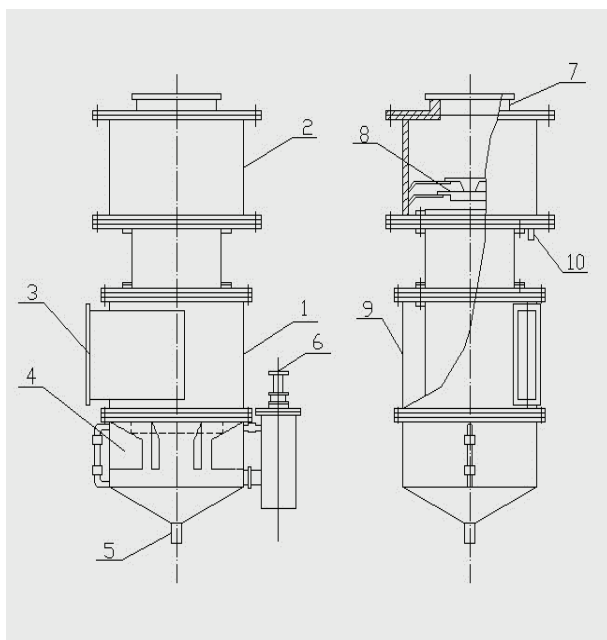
Схема инжекционно - пенного аппарата II - ой ступени очистки: 1 - корпус аппарата, 2 - корпус влагоотделителя, 3 - тангенциальный патрубок, 4 - лопаточный закручиватель, 5 - штуцер для удаления отработавшей жидкости, 6 - штуцер ввода рабочей жидкости, 7 - патрубок для выхода очищенного воздуха, 8 - тарельчатый сепаратор, 9 - контактно - выхлопная труба, 10 - штуцер вывода рабочей жидкости.
